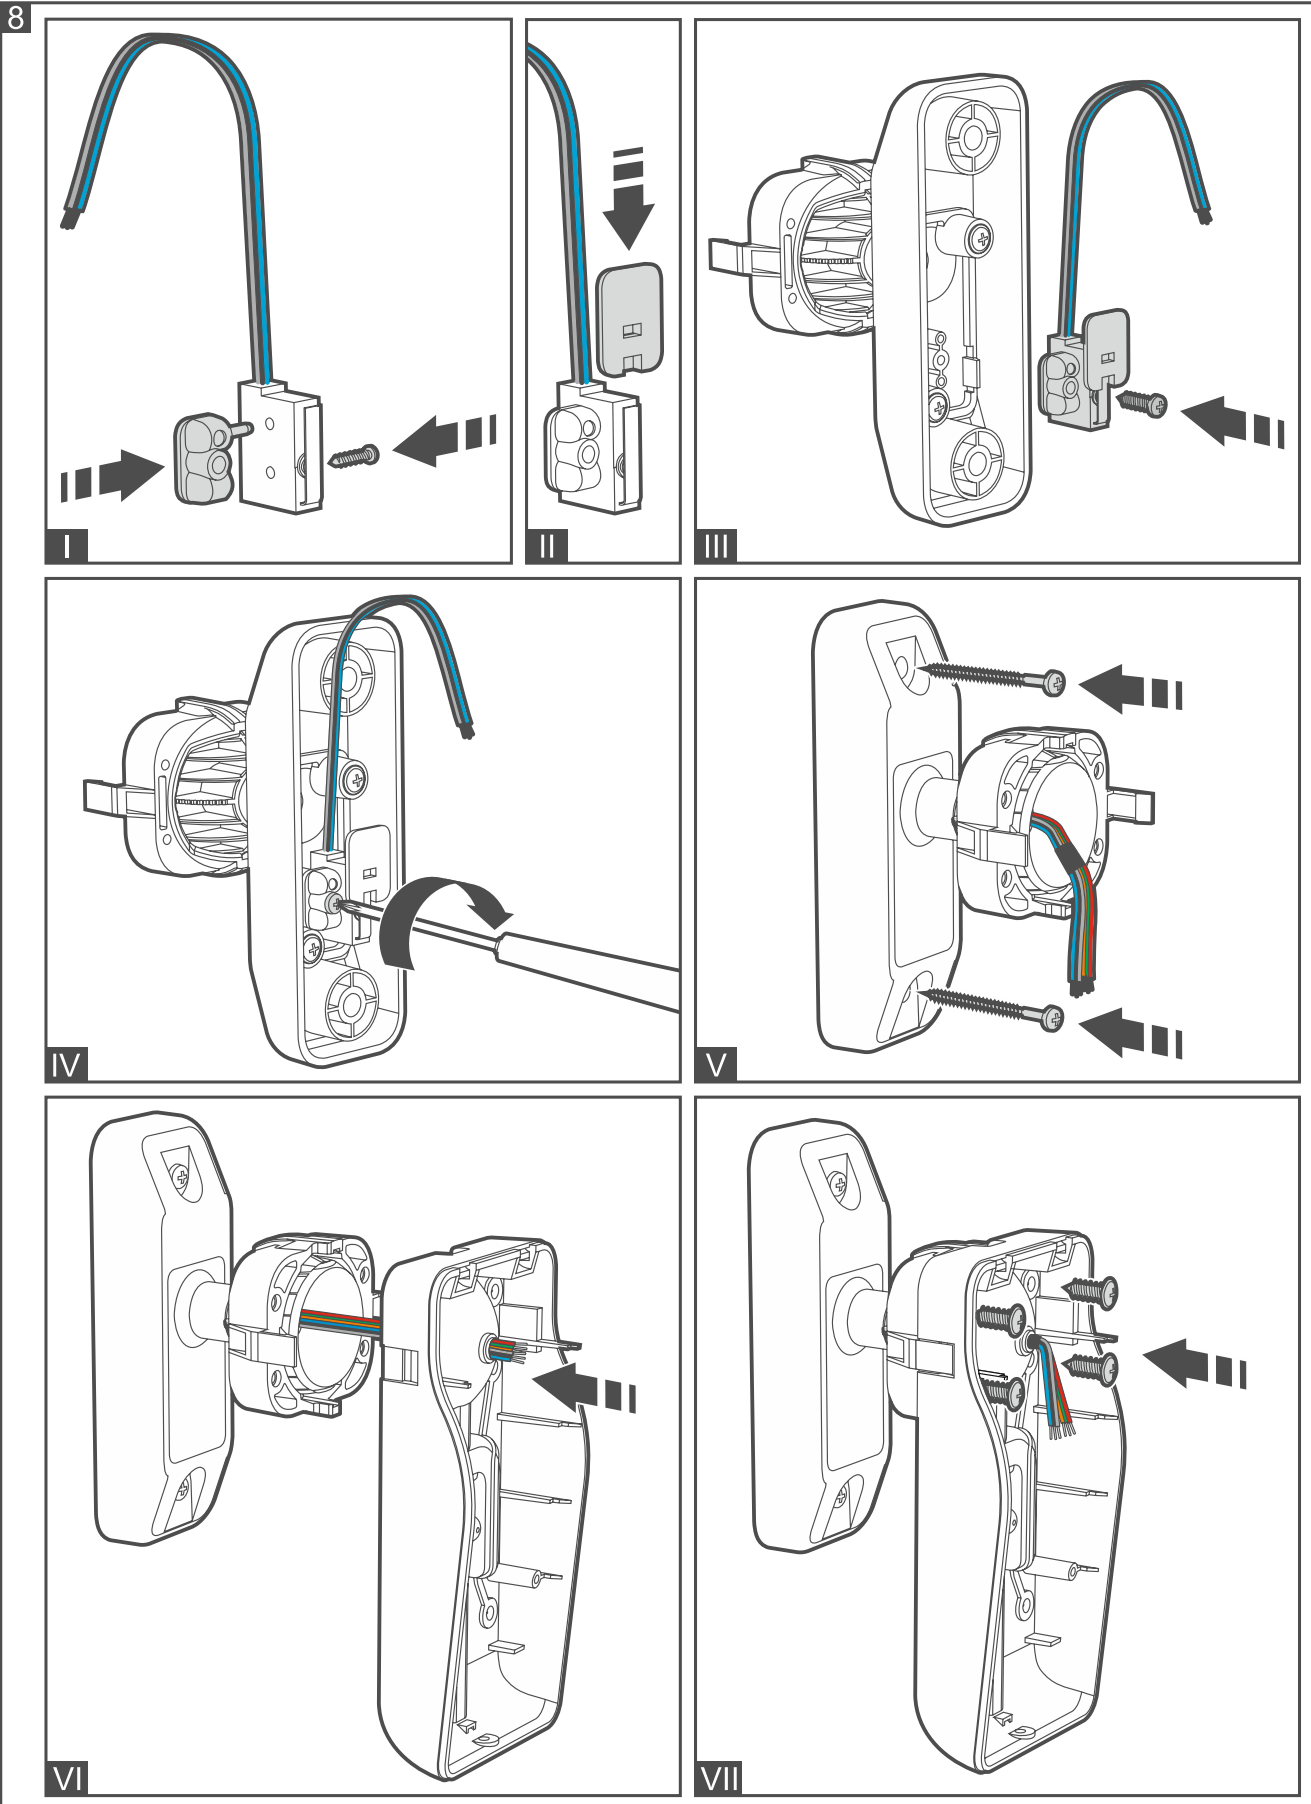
ilustruje montaż styku sabotażowego w jednej z dwóch dopuszczalnych pozycji. Miejsce montażu styku sabotażowego zależy od sposobu montażu uchwytu kąтового. Jeżeli styk sabotażowy ma być zamontowany w drugiej pozycji, uchwyt do montażu styku umieść z drugiej strony.
